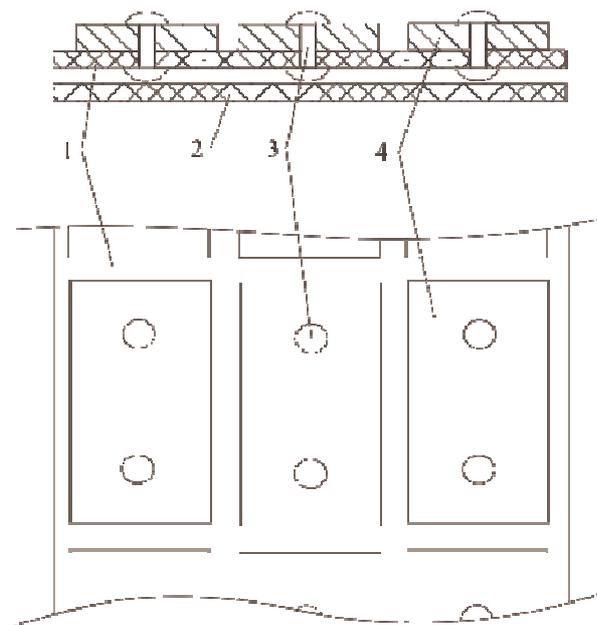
Альтернативный тип обшивки корпуса гидродинамического обтекателя: 1 – первый слой брезента, 2 – второй слой брезента, 3 – заклепка, 4 – защитный щиток.
